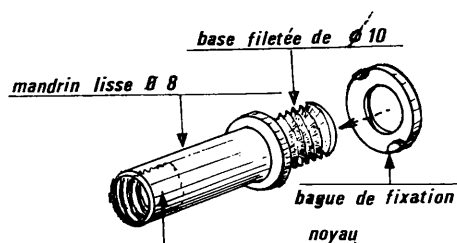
Type classique de mandrin du bobinage HF. Le noyau est long de 9 mm, diamètre 6,5 mm.
